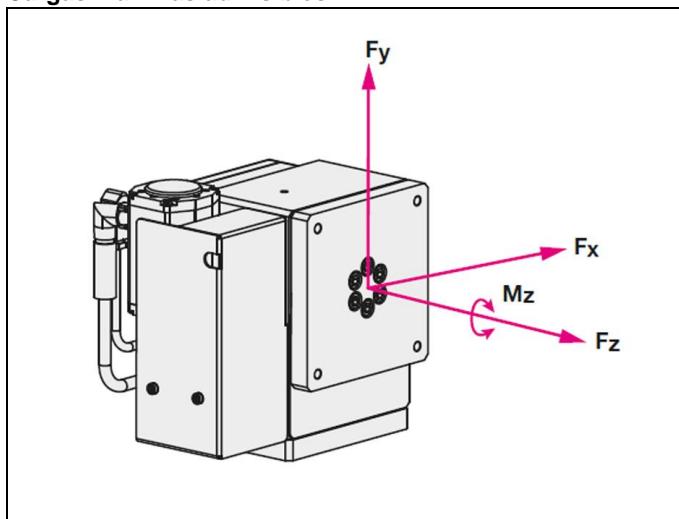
Ejes de las fuerzas y los pares de giro aplicados, horizontal
